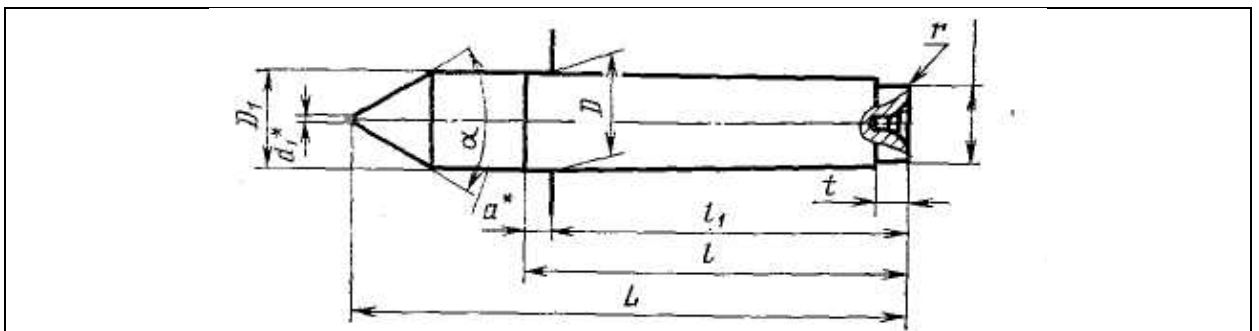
Конструктивні параметри упорного центру, які нормуються стандартом ГОСТ 13214-79
